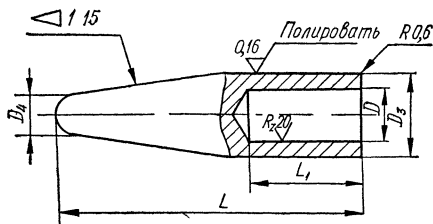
Оправка для установки уплотнительных колец в наружные канавки.
